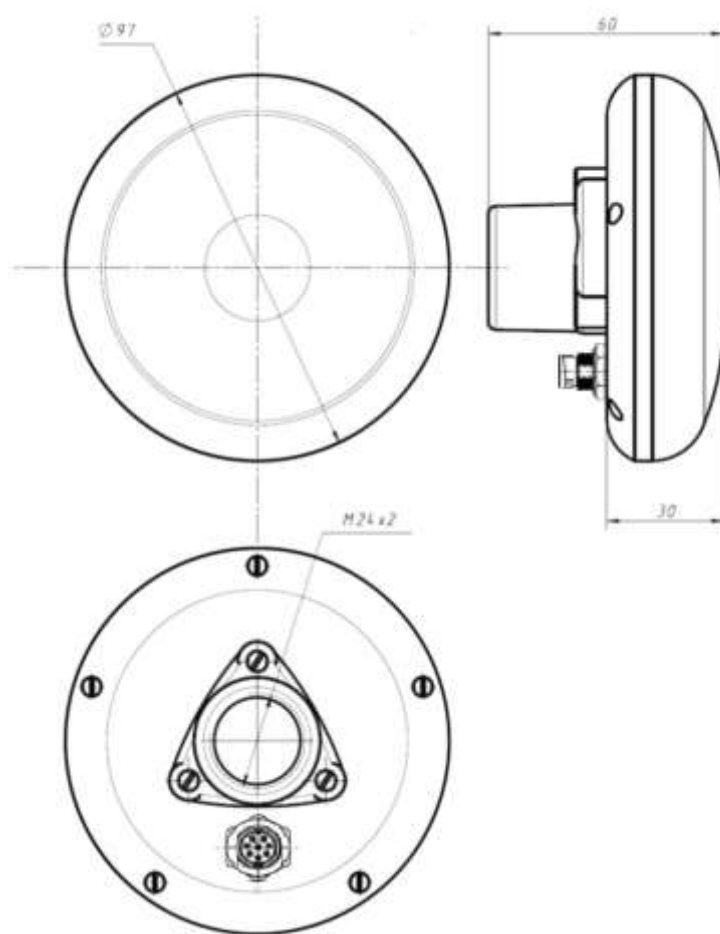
Габаритные и присоединительные размеры изделия
